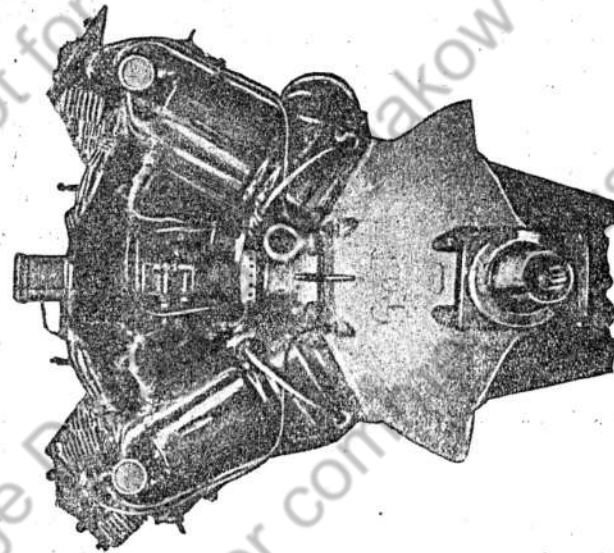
Вид на двигатель со стороны носка коленчатого вала, на который надевается маховик.
